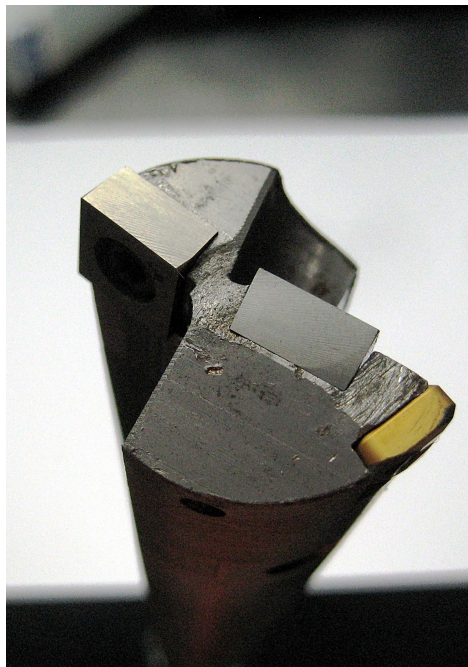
Probenplattenfixierung mit Klemmschrauben
